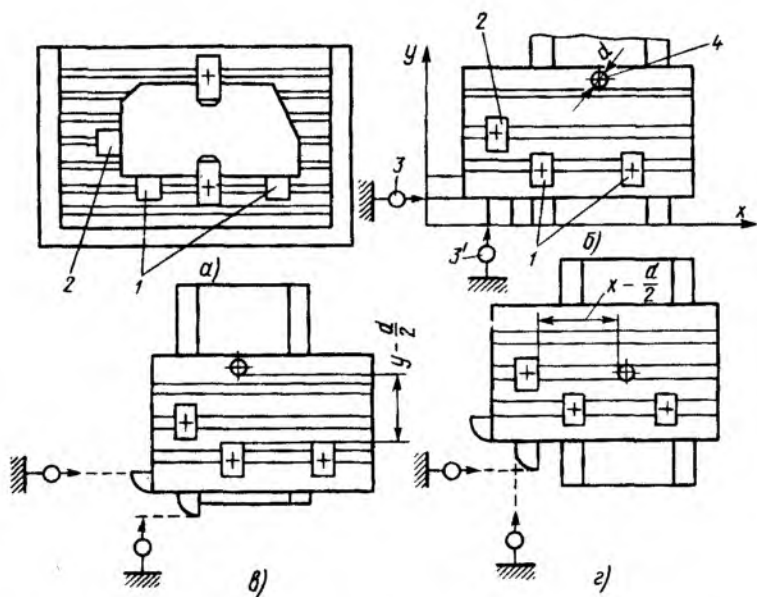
Схема базирования заготовки на столе фрезерного станка: *а* – установка заготовки в „координатный угол”; *б* – установка базирующих элементов; *в* – измерение расстояния от оправки до направляющей базы; *г* – измерение расстояния от оправки до опорной базы
